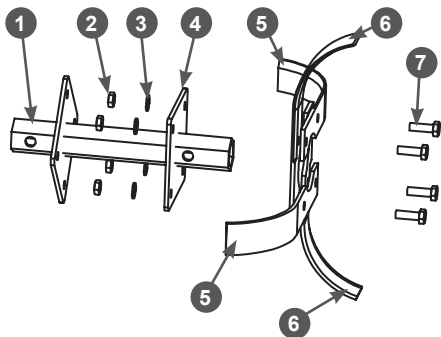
Установка ножей на внутренний фланец основной секции оси фрезы
